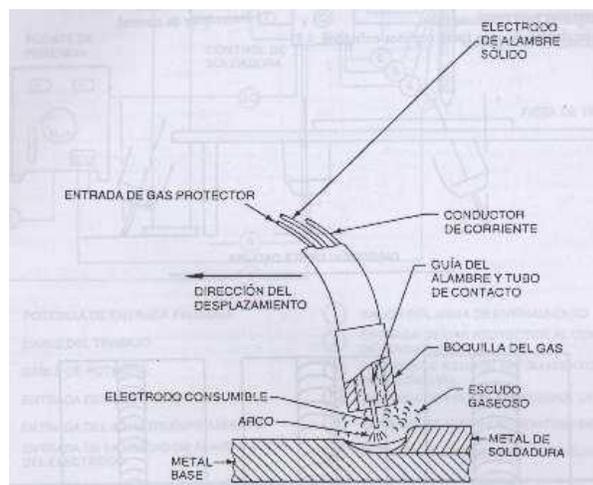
Soldadura eléctrica por arco con alambre sólido como electrodo y protección gaseosa GMAW. Estructura de la soldadura.¹⁷
